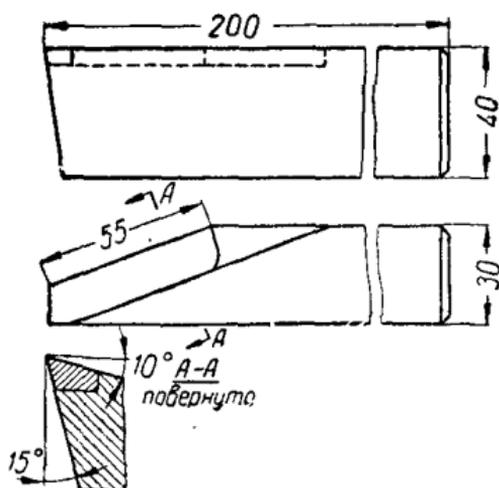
Обычный резец для нарезания левой резьбы червяка.
